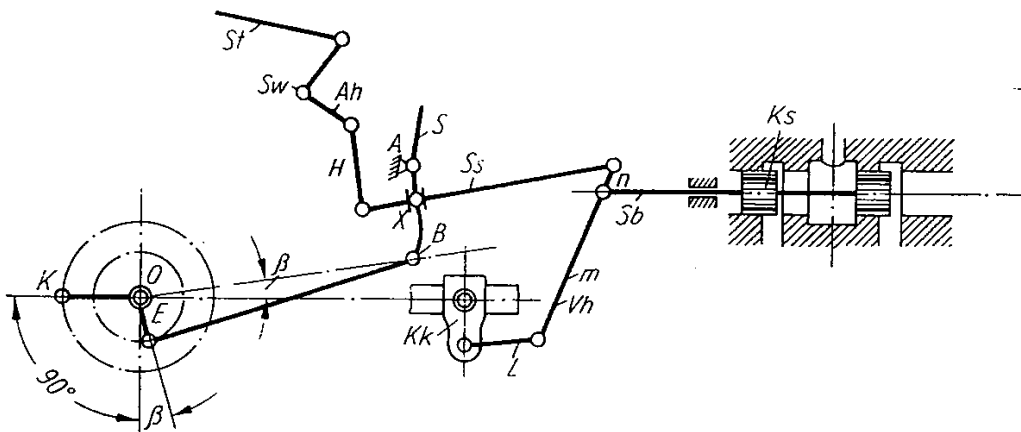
Schema der Heusinger-Steuerung mit Hängeeisen
